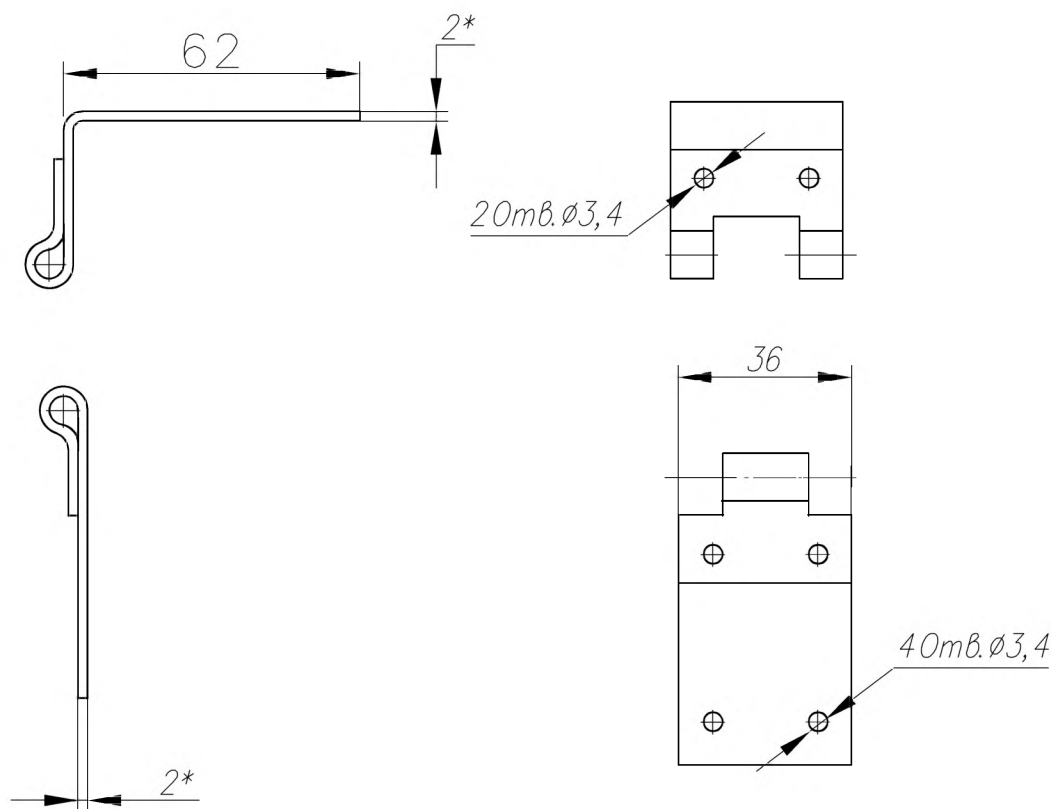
Части чертежа, подготовленные для «сборки»
